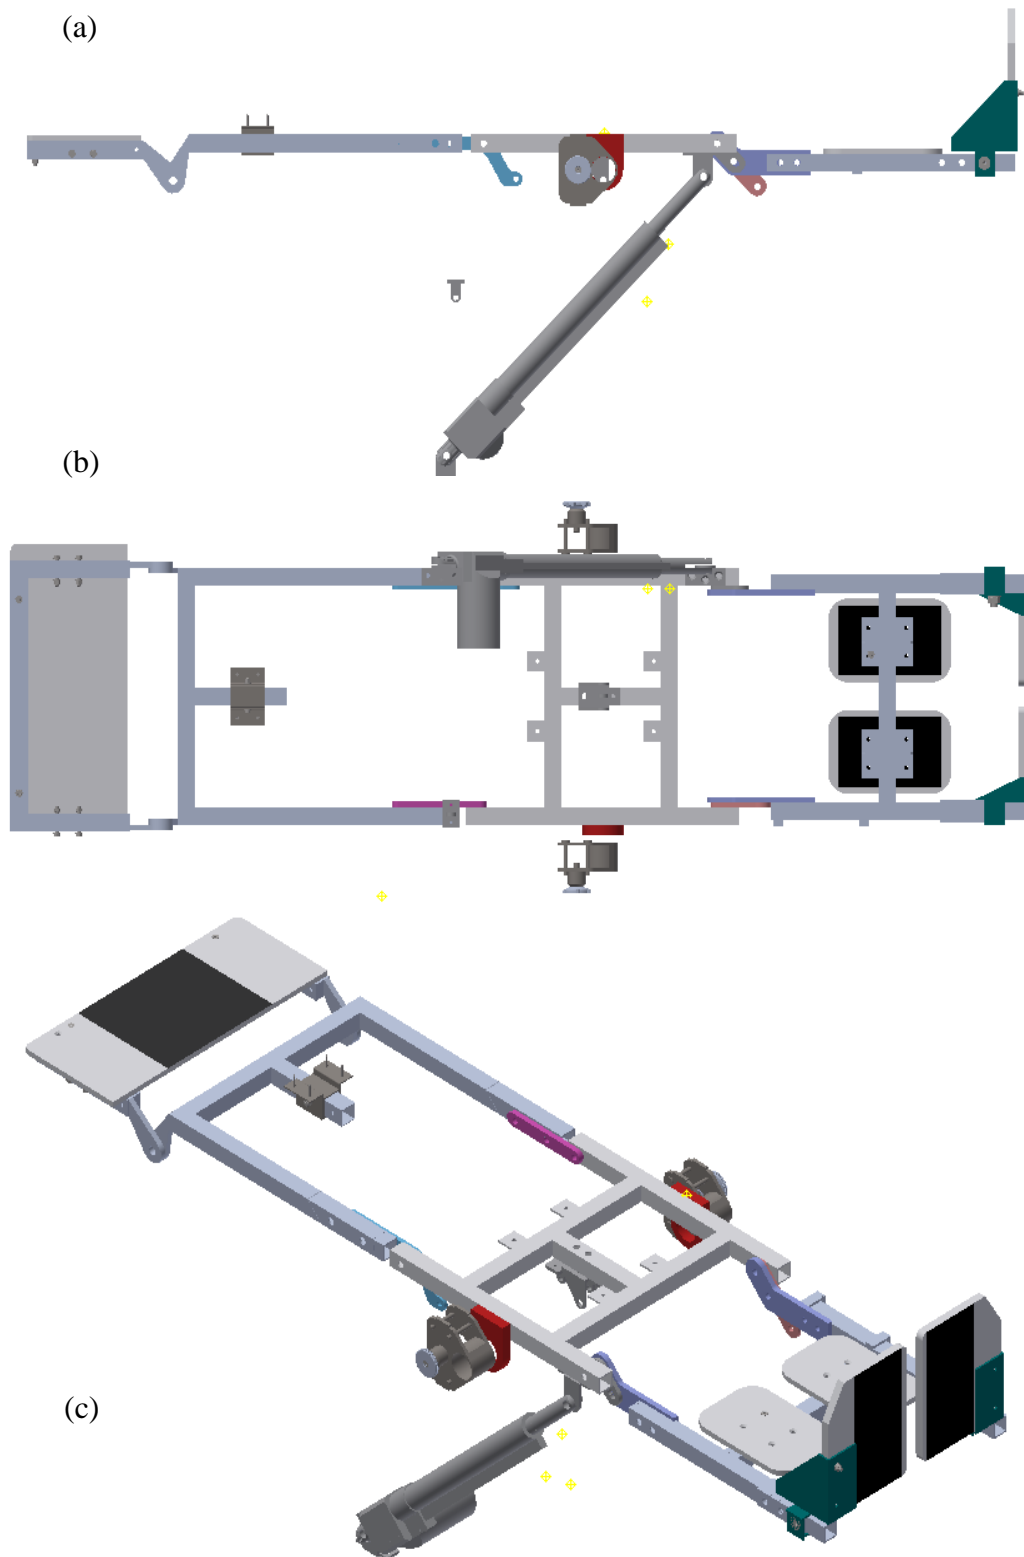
Giro del asiento - Vista isométrica, (b) Vista frontal
